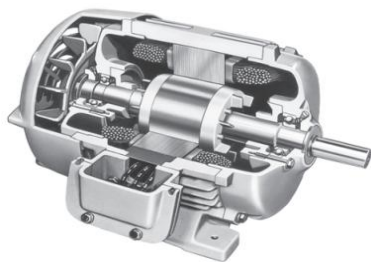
Motor de indução trifásico com rotor gaiola de esquilo [9].
